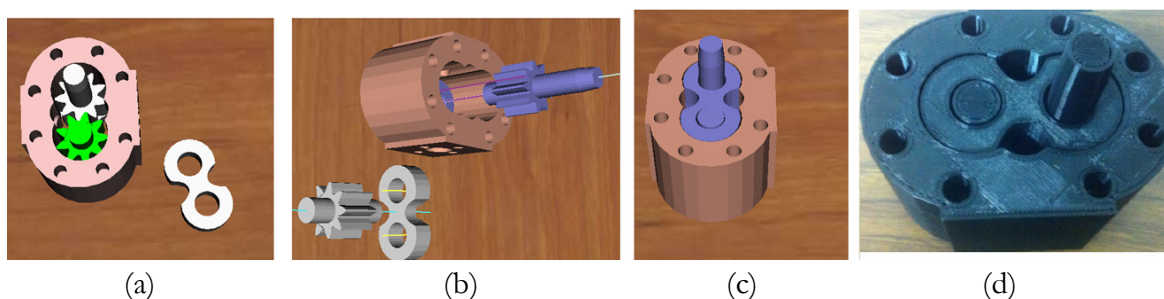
Bomba de engranes: (a) ensamble utilizando únicamente PBM, (b) ensamble utilizando PBM y DACs, (c) ensamble final, (d) ensamble real.
